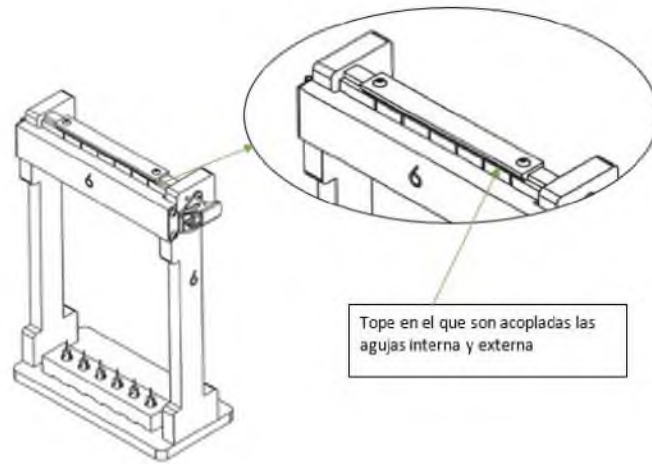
Drawing del Fixture UV para ensamble de las agujas
